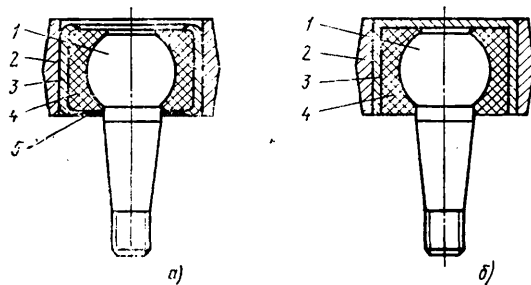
Ремонт шаровых соединений с обоймой (а) и со стаканом (б): 1 — шаровой палец; 2 — корпус; 3 — обойма (стакан); 4 — наполнитель; 5 — обжим
